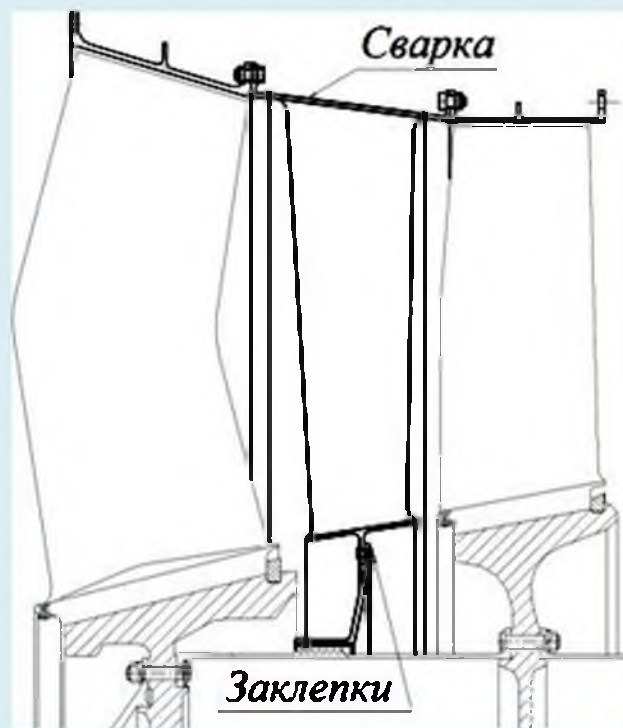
Разборный НА компрессора СД ТРДД НК-56:
